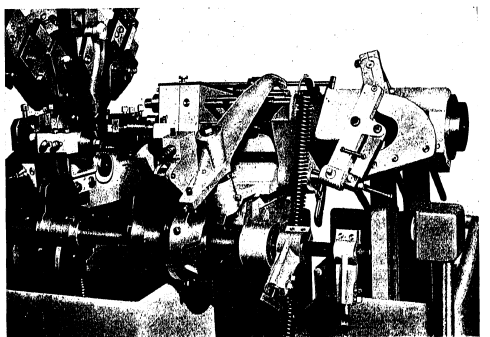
SCHWENKBARER WERKZEUGKOPF HW-17a
